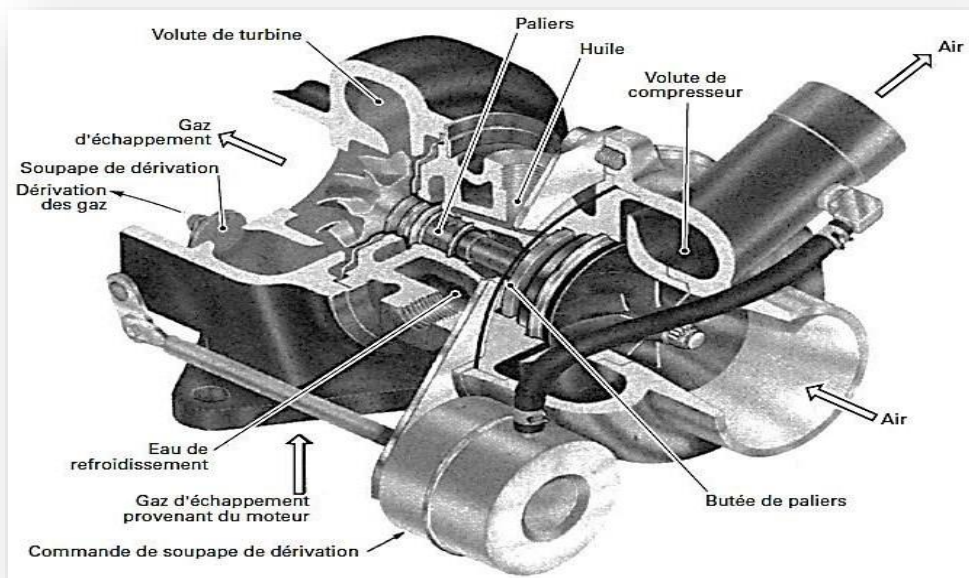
Écorché de turbocompresseur d'automobile [9]
